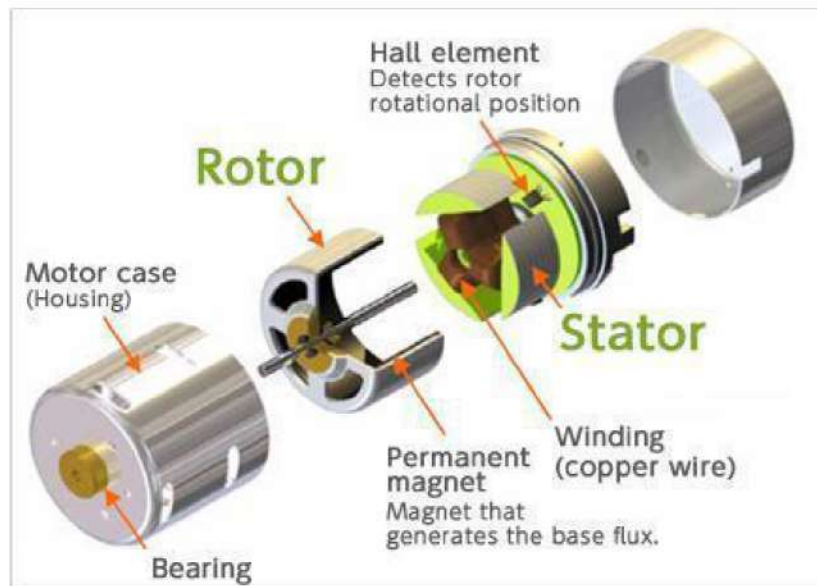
Motor BLDC; rotor por fora do stator; Fonte: Nidec Corporation: Brushless Motors
